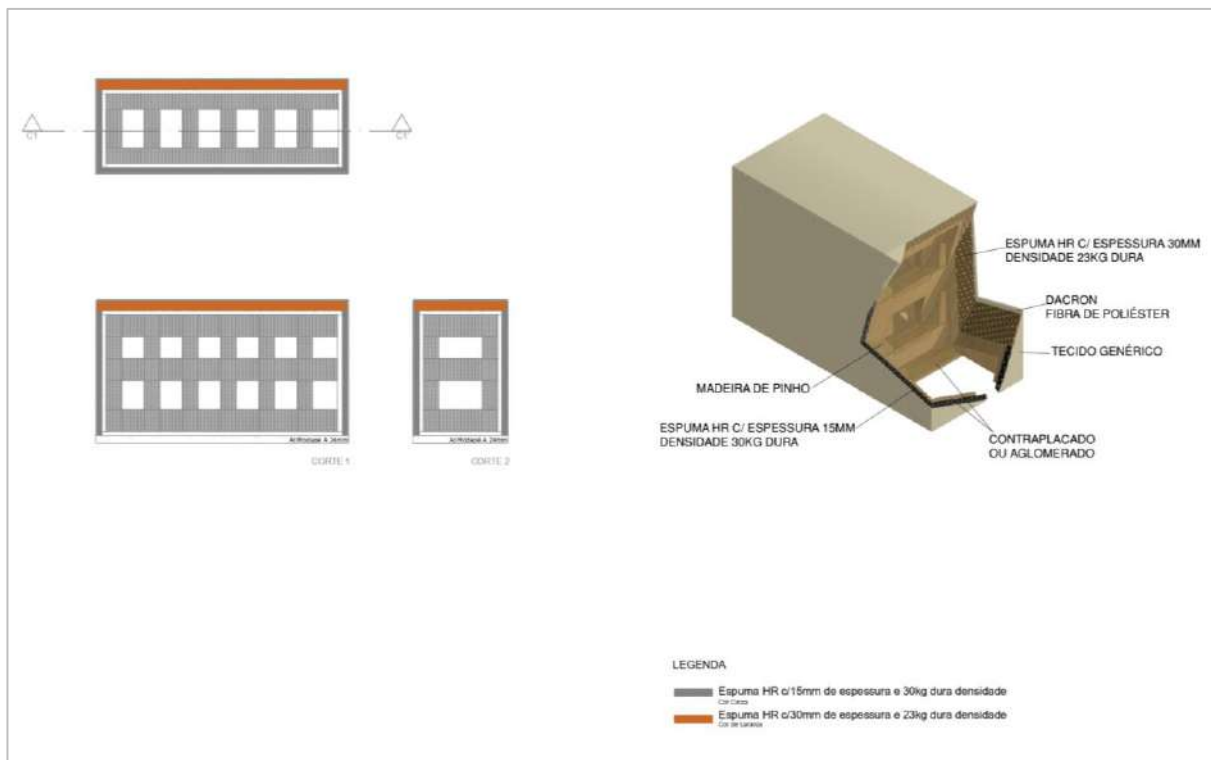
Desenhos técnicos-Cortes sofá módulo C. Fonte: Júlia Rodrigues
